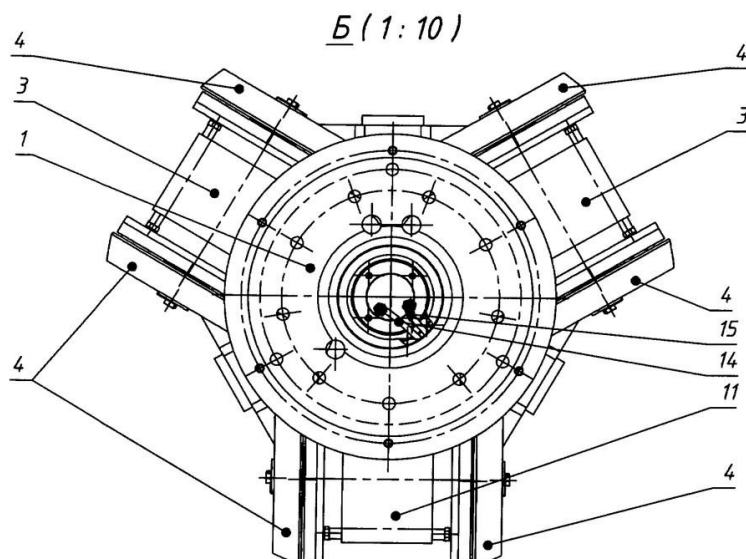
Механизм перемещения машины для сварки труб, в дальнейшем "механизм перемещения", вид Б
